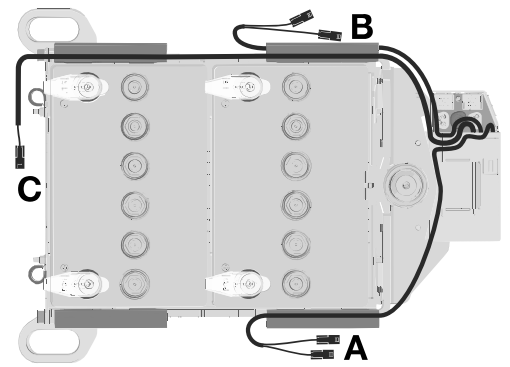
Die Hauptkabel für die vordere Beleuchtung und Blinker sind am Motorkabel befestigt.
